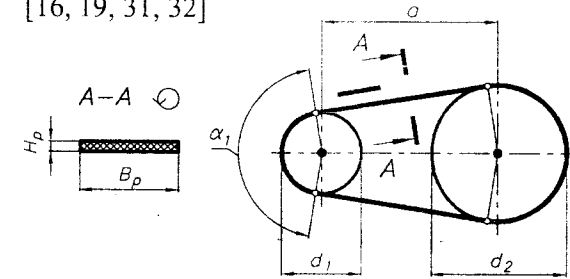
Схема и основные размеры плоскоременной передачи
